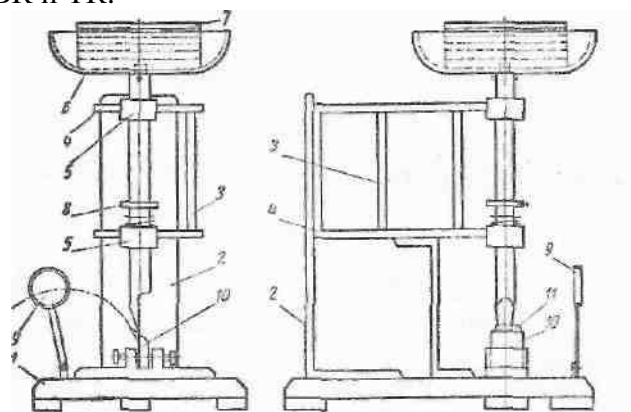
Прибор для измерения силы сцепления нароста: 1 — основание; 2 — стойка; 3 — стяжной болт; 4 — щека; 5 — подшипник скольжения; 6 — чаша для груза; 7 — груз; 8 — фиксирующее кольцо; 9 — оптический окуляр; 10 — испытываемая пластинка (твердого сплава); 11 — нарост
